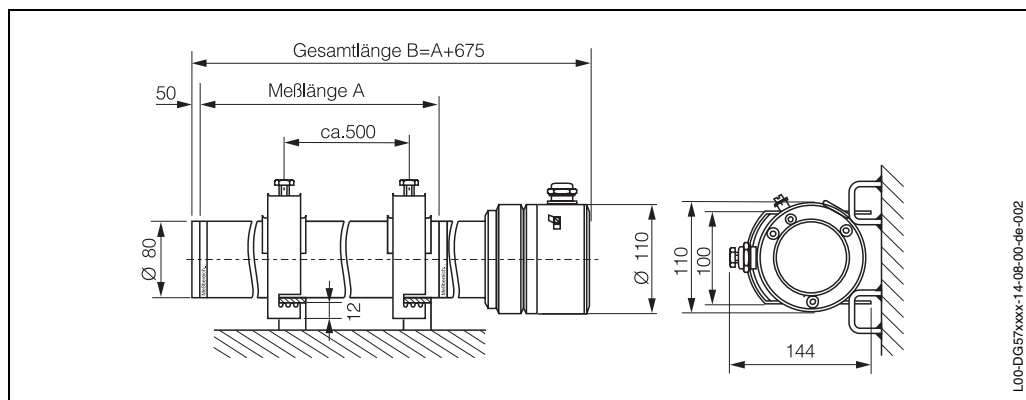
Detektor DG 57: Abmessungen in mm
